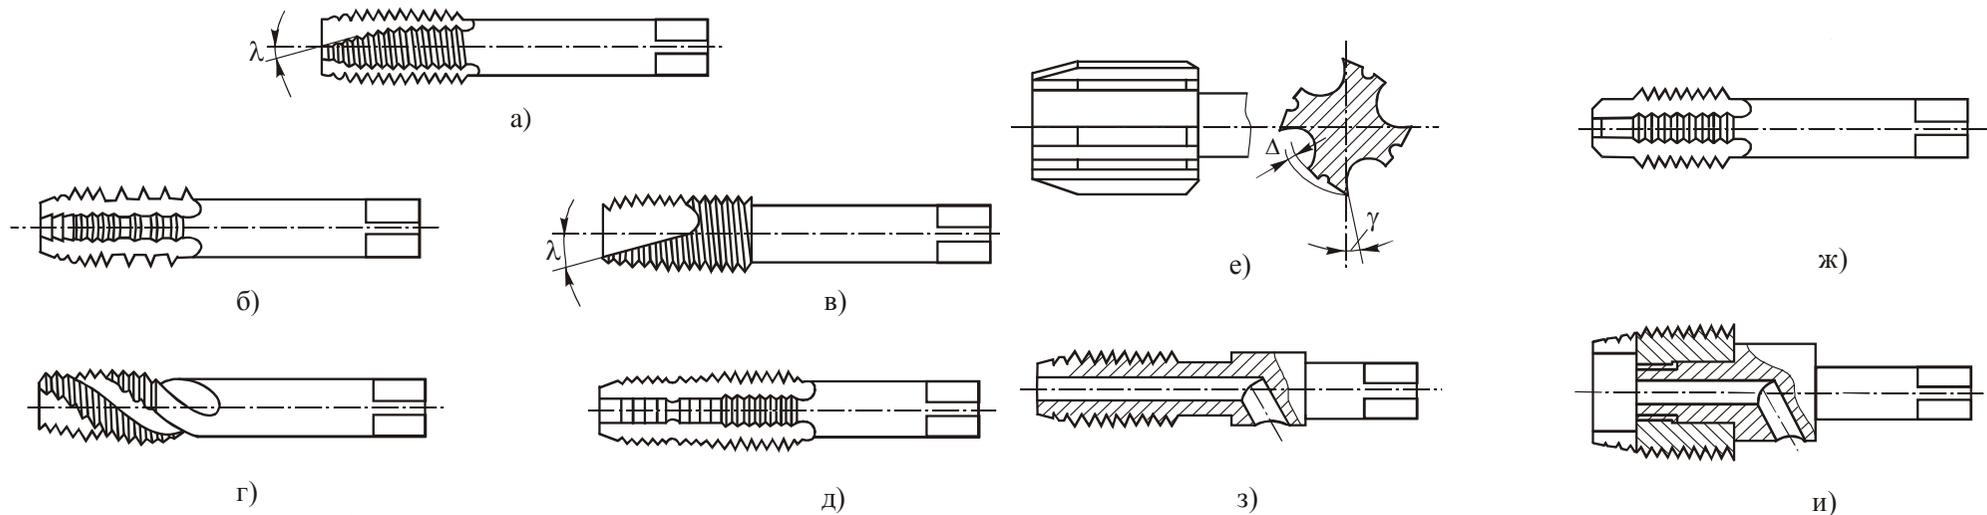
Конструкции некоторых типов метчиков: *а* – слесарный (ручной); *б* – с шахматным расположением зубьев; *в* – бесканавочный; *г* – с винтовыми канавками; *д* – ступенчатый; *е* – с режуще-выглаживающими зубьями; *ж* – с направляющей частью; *з* – с внутренним подводом СОЖ; *и* – колокольного типа
